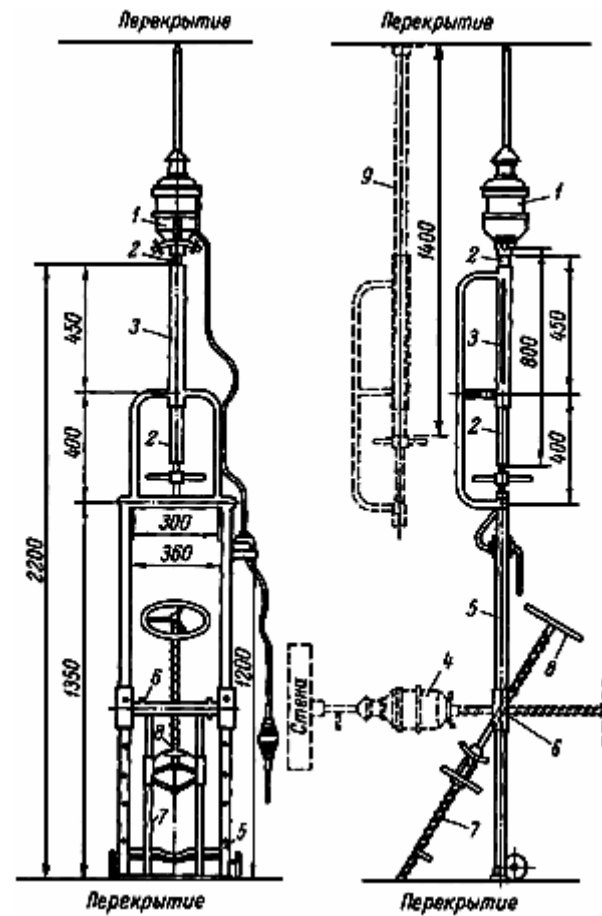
Станок-стойка для сверления отверстий в полах, потолках и стенах
